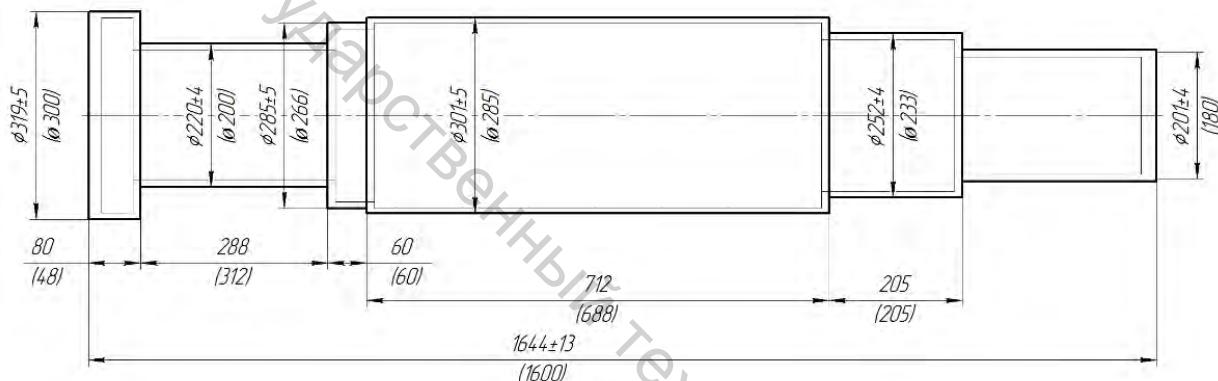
Эскиз поковки с основными и дополнительными припусками и допускаемыми отклонениями
